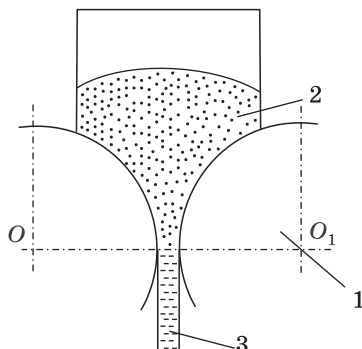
Схема прокатки нанопорошков: 1 — вал; 2 — порошок в загрузочном устройстве; 3 — получаемая заготовка
